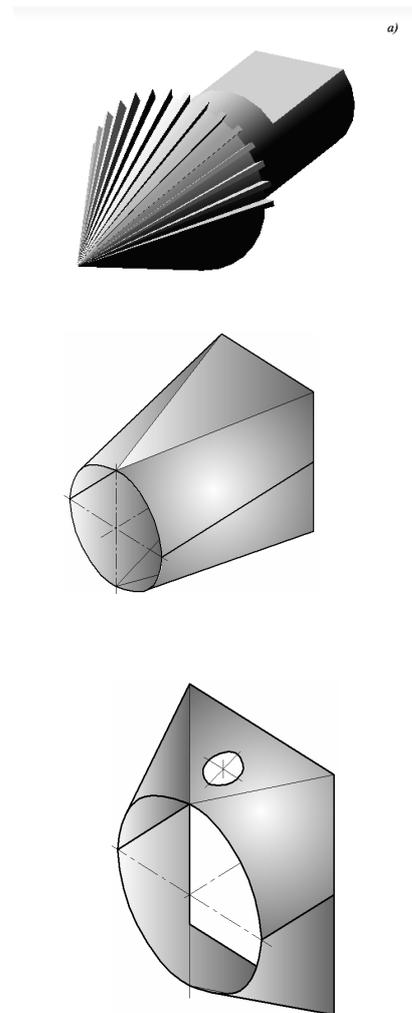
Пуансон и детали, полученные вдавливанием жесткого инструмента в заготовку
